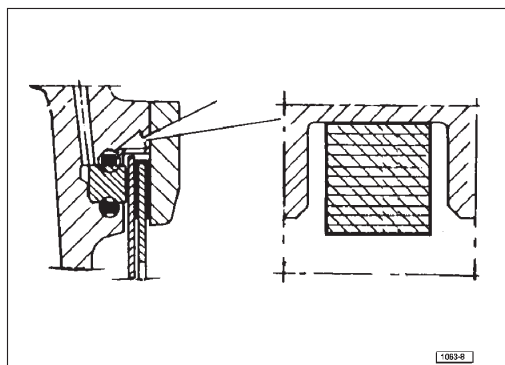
Montage de la bague d'étanchéité du piston de compression des freins avant.
